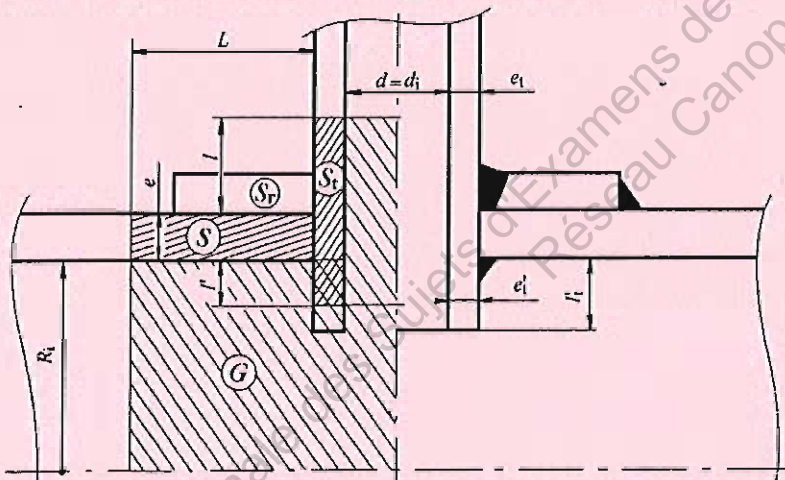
1 - Ouverture de tubulure soudée normale à la paroi d'une enveloppe cylindrique avec anneau-renfort rapporté et tubulure dépassante.
